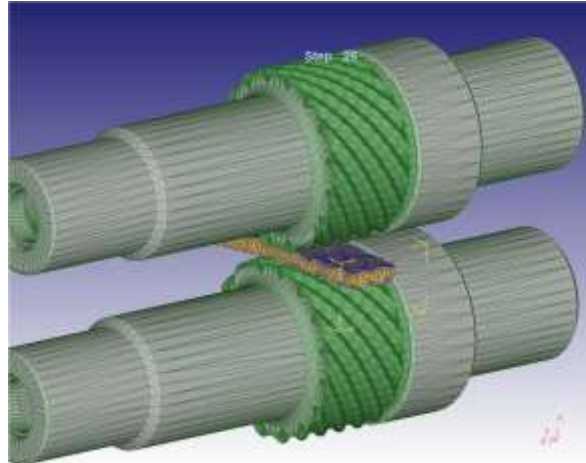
Внешний вид рабочей поверхности прокатных валков
